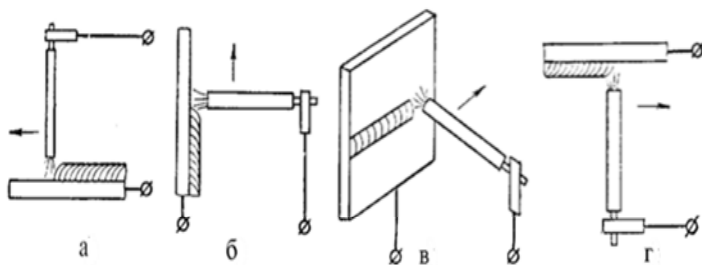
Возможные пространственные положения шва при ручной электродуговой сварке: а - нижнее; б - вертикальное; в - горизонтальное; г – потолочное
